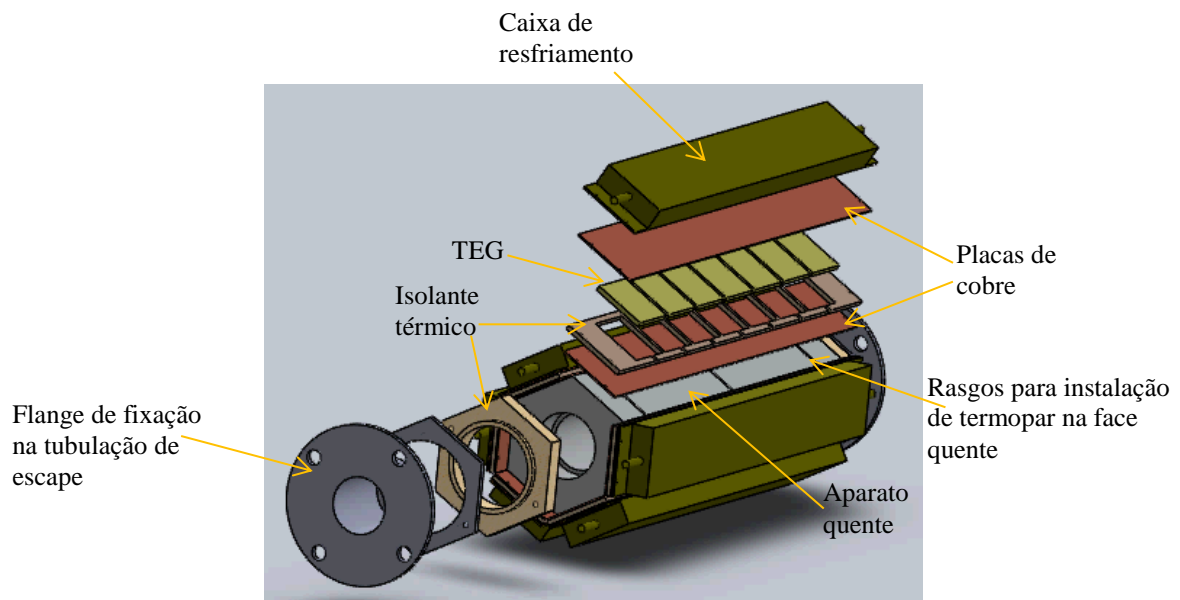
Projeto da Planta de Geração Termoelétrica
